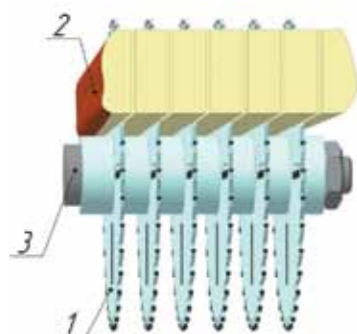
Работа многопильного станка: 1 – пила; 2 – заготовка; 3 – пильный вал
